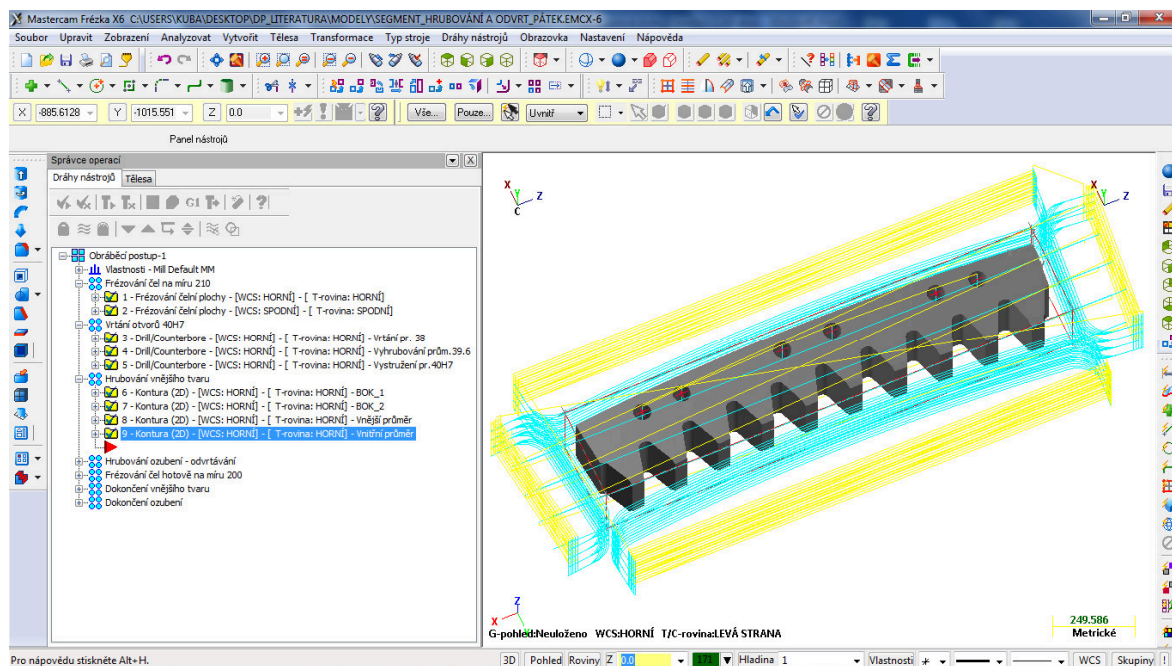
Segment po ohrubování vnějšího tvaru – operace 5
